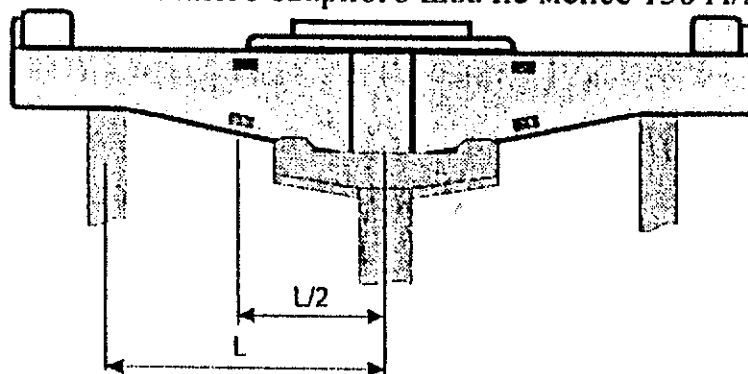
Положение основания ФП при измерении напряженности магнитного поля на поверхности надрессорной балки (вид сбоку)
